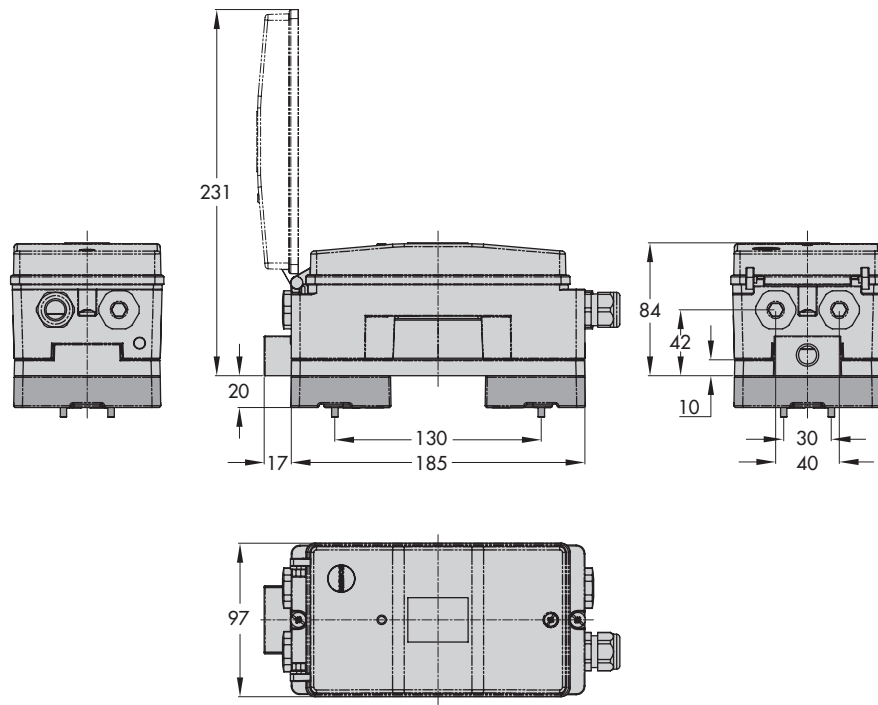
Ausführung für externes Magnetventil Typ 3738-20-xxx1000xxx200
